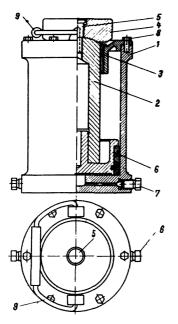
Гидродомират конструкции ВНИМИ грузоподъемностью 100 т:
